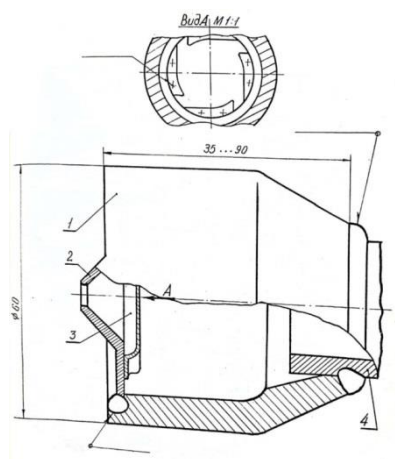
Конструкция форсунки подачи мазутного топлива. 1 – головка форсунки; 2 – сопло; 3 – завихритель; 4 – штанга подачи мазута.
